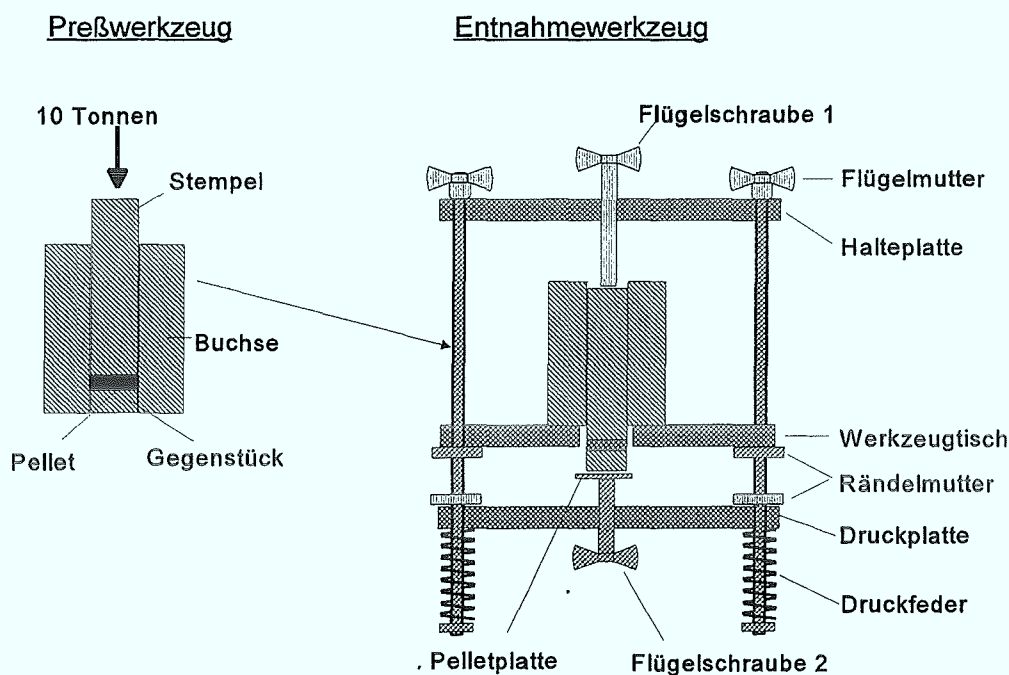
Presswerkzeug und Entnahmewerkzeug zur Pelletherstellung
